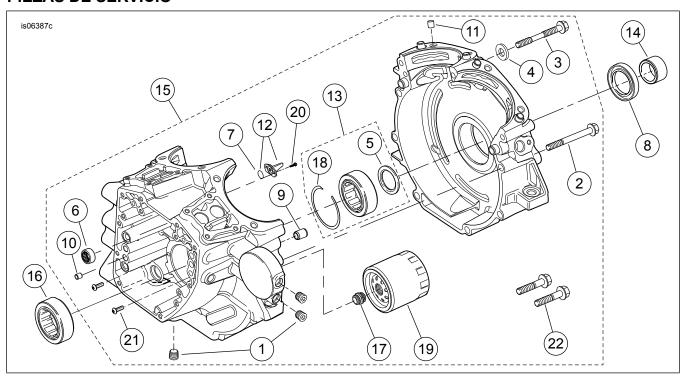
Cárter, filtro de aceite y enfriador del motor ensamblado Screamin' Eagle Pro SE120R (Alfa)
